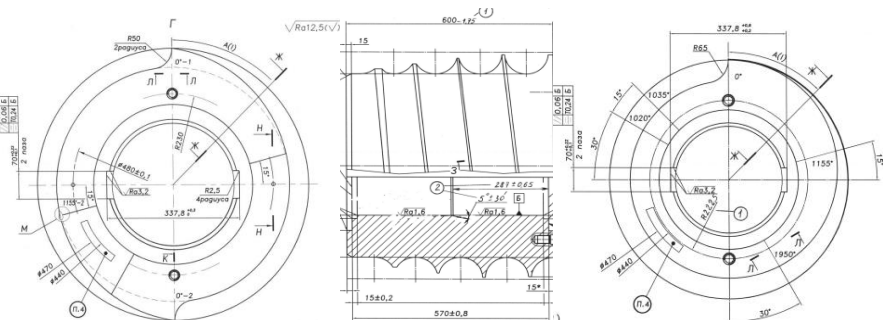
Прокатный валок с однозаходной калибровкой для прокатки шаров диаметром 120 мм
